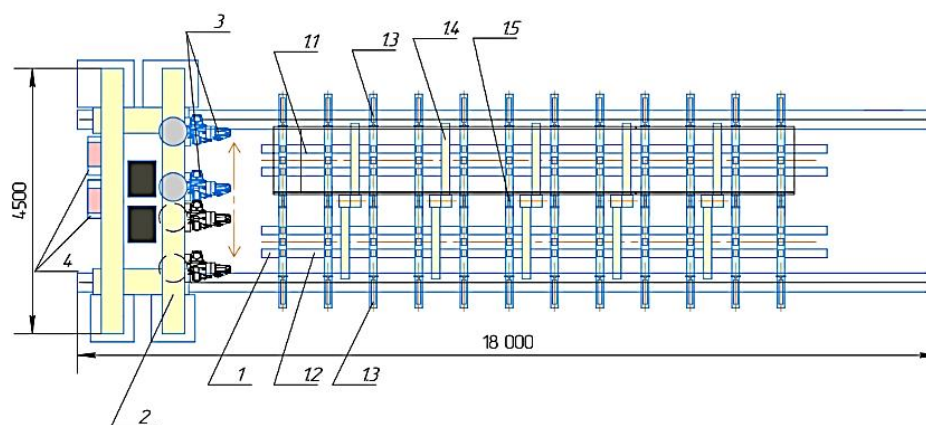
Установка для автоматичного складання та зварювання двотаврових балок:
